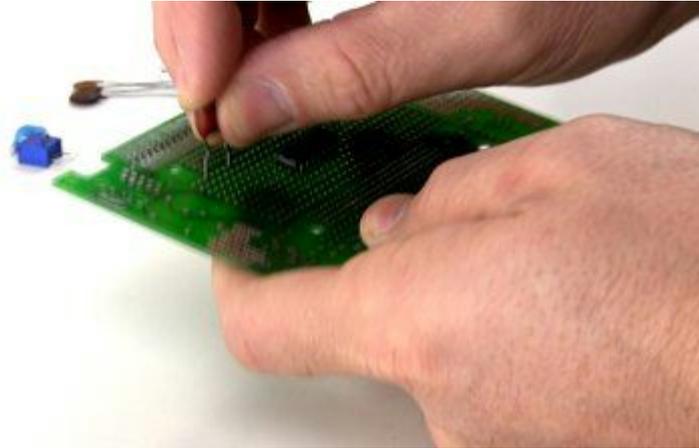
Inserción de componentes de taladro pasante a mano.
